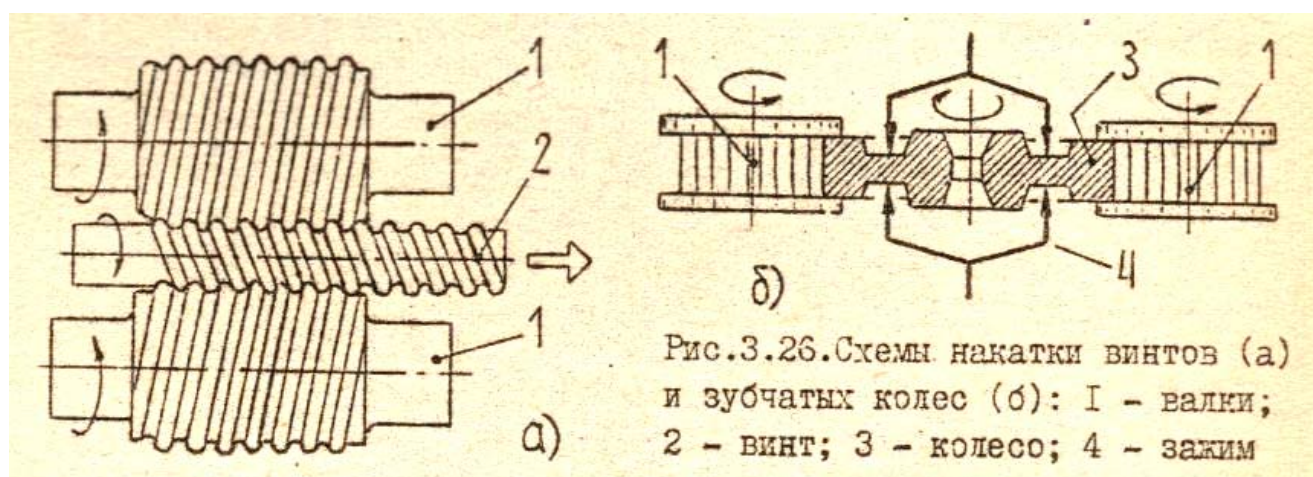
Схемы накатки винтов (а) и зубчатых колес (б):
